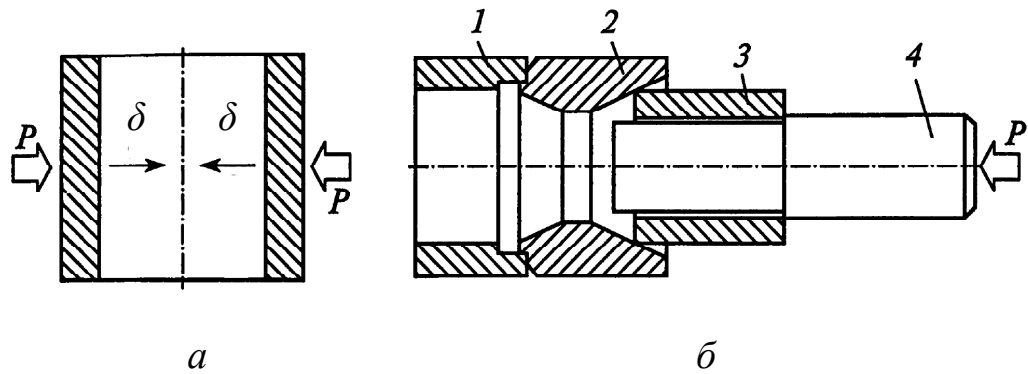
Пластическое деформирование обжатием: *a* – принципиальная схема; *б* – приспособление для обжатия втулок; 1 – опорная втулка; 2 – матрица; 3 – восстанавливаемая втулка; 4 – оправка
